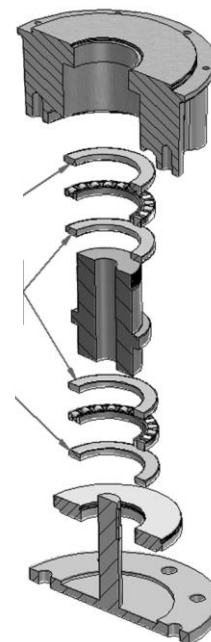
Шток арматуры в сборе с цилиндрическими роликовыми подшипниками
